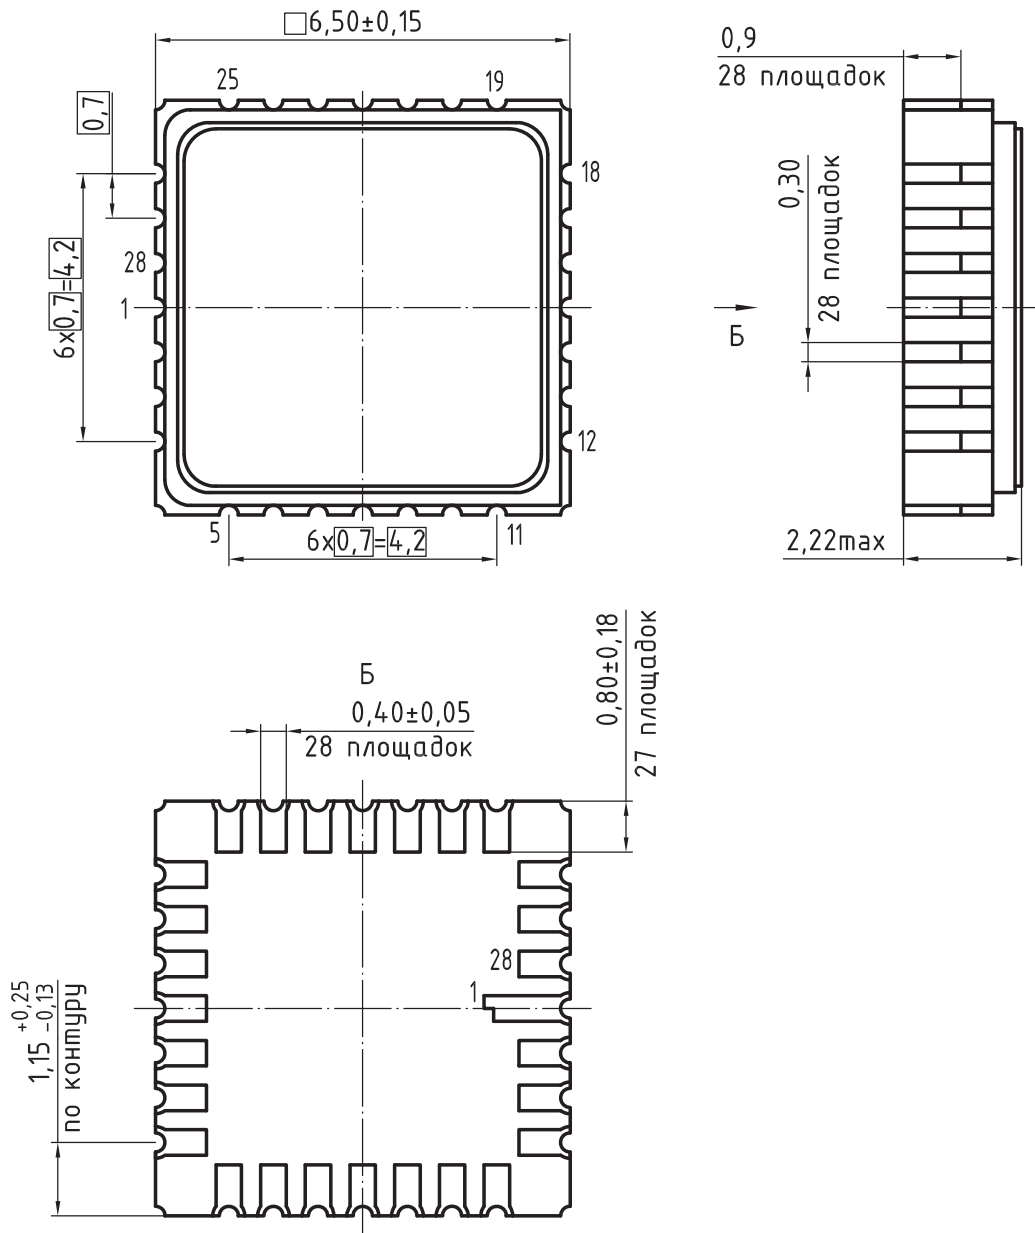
Чертеж корпуса МК 5123.28-1.01
